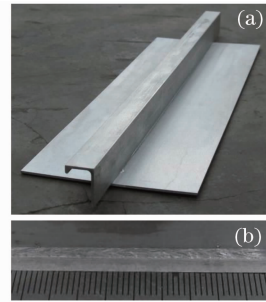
(a) T 型接头试样及 (b) 焊缝表面
